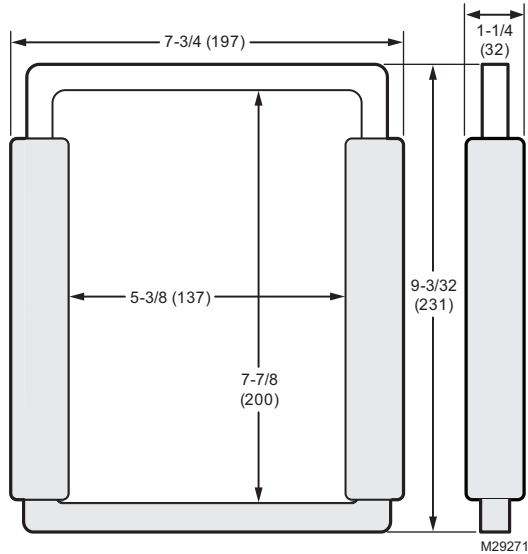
Dimensions du capteur de courant 3200 A en po (mm).
